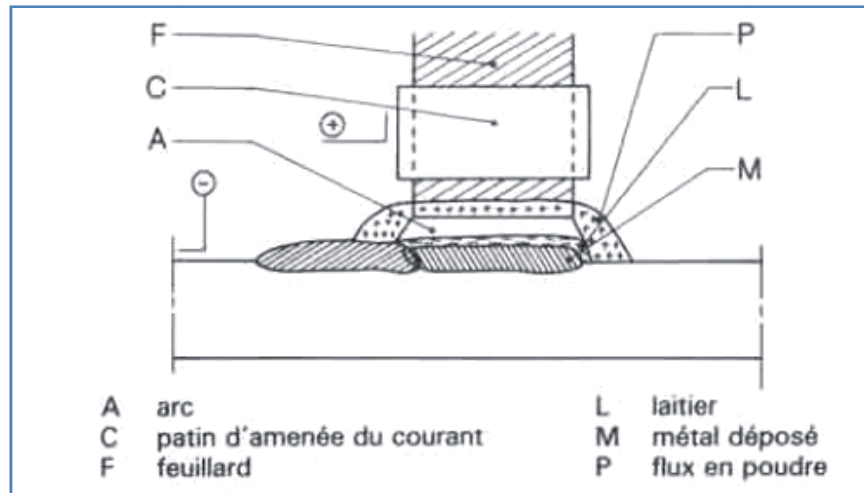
principe de soudage sou flux gazeux [16].
